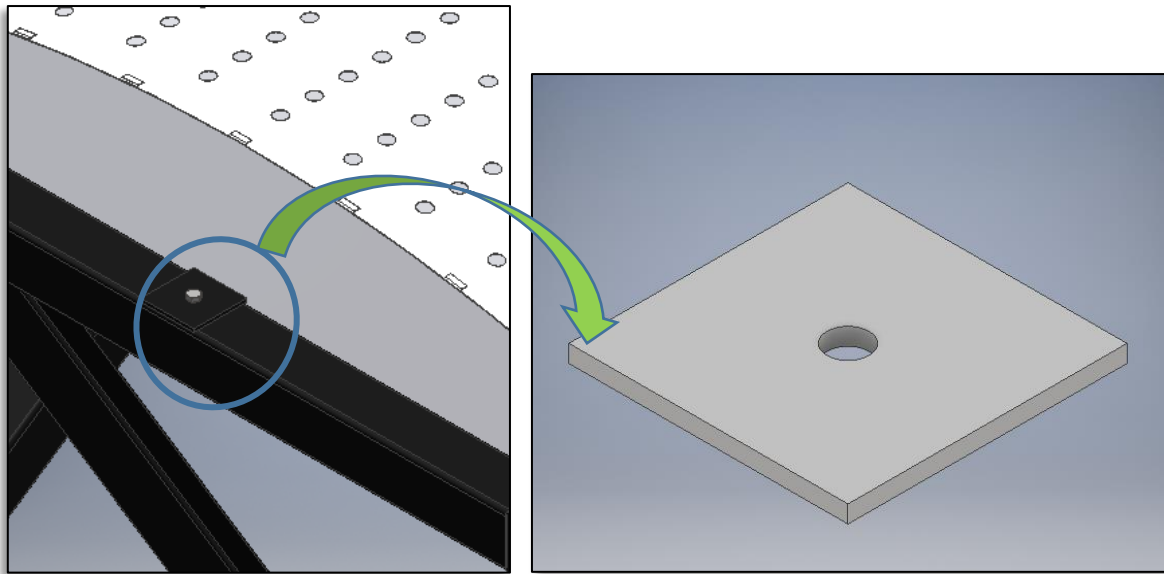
Placas para montaje de plato inferior y drenaje.
